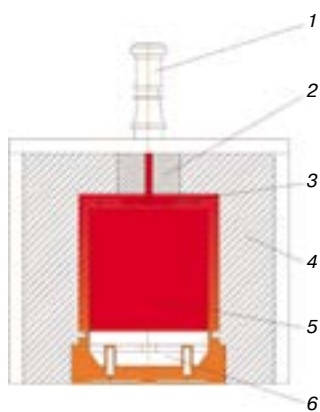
Схема установки жарового вентилятора в своде печи: 1 – двигатель вентилятора; 2 – съемная теплоизоляция; 3 – крыльчатка вентилятора; 4 – футеровка печи; 5 – садка изделий на вагонетке; 6 – вагонетка
